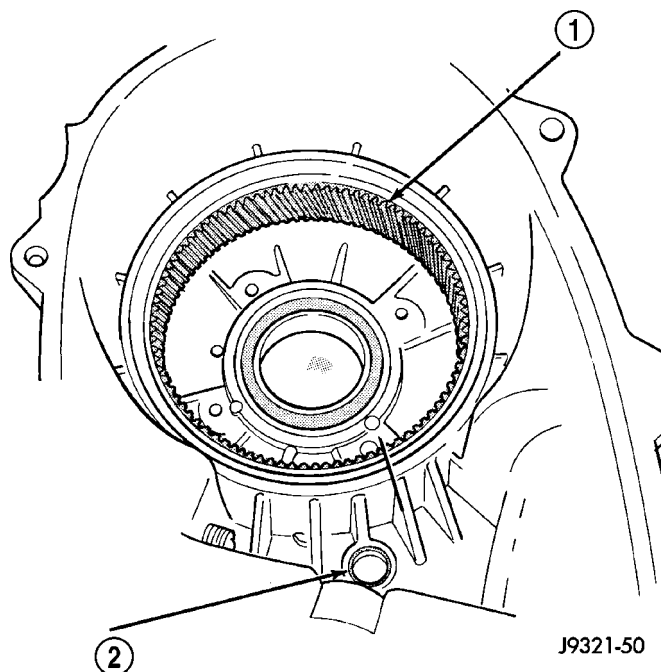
Emplazamiento del engranaje anular de posición de baja
